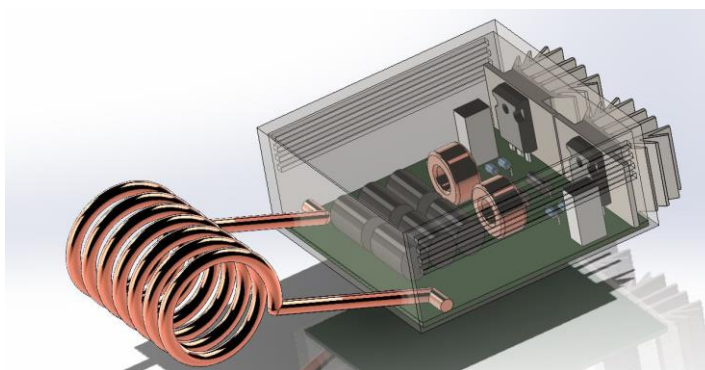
Корпус индукционного нагревателя *CompactTool 1000B
